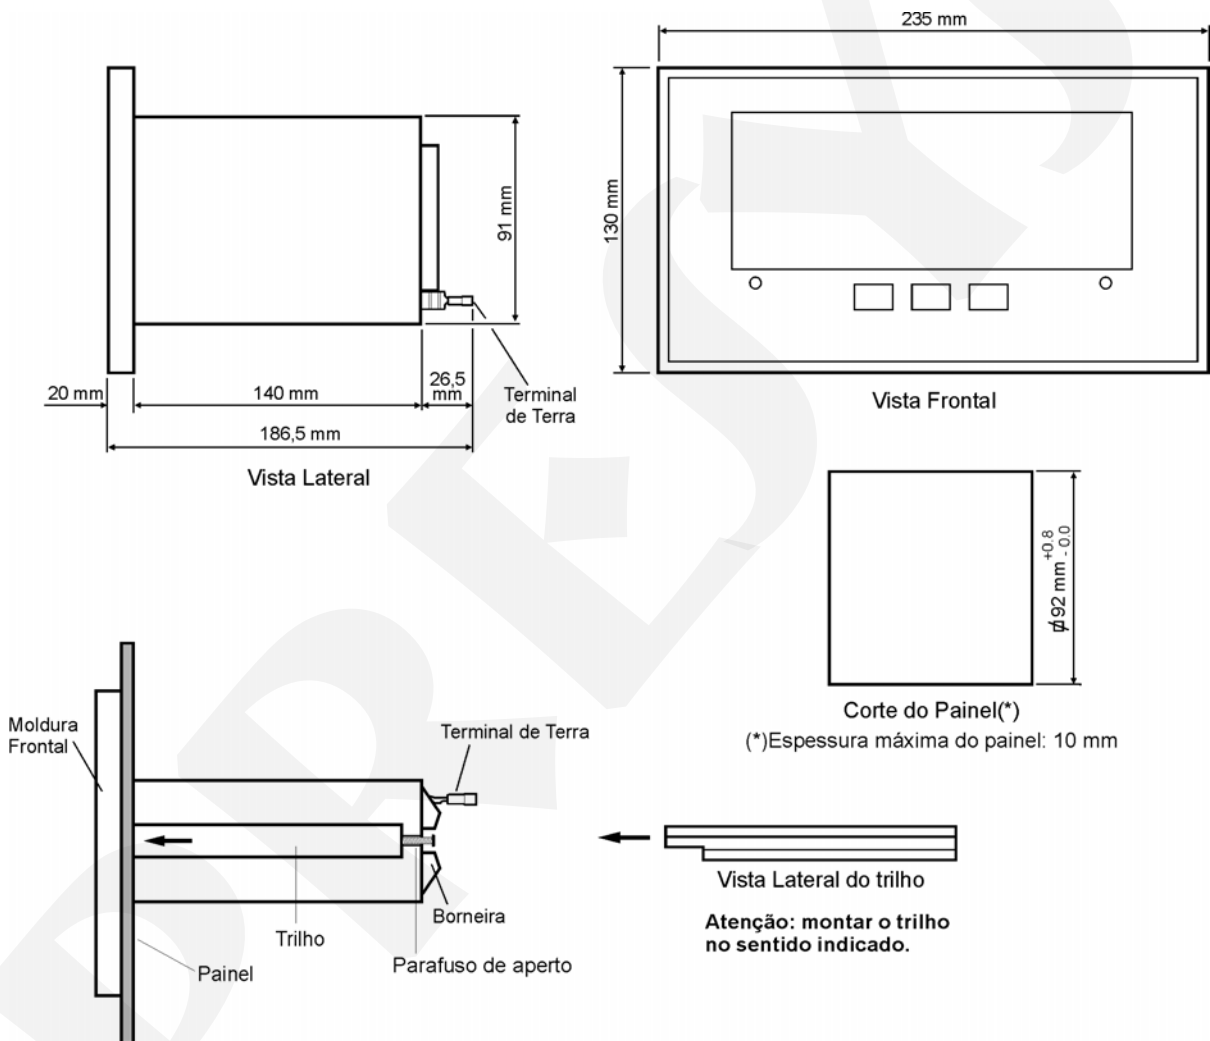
Desenho dimensional, corte e vista lateral da montagem no painel
